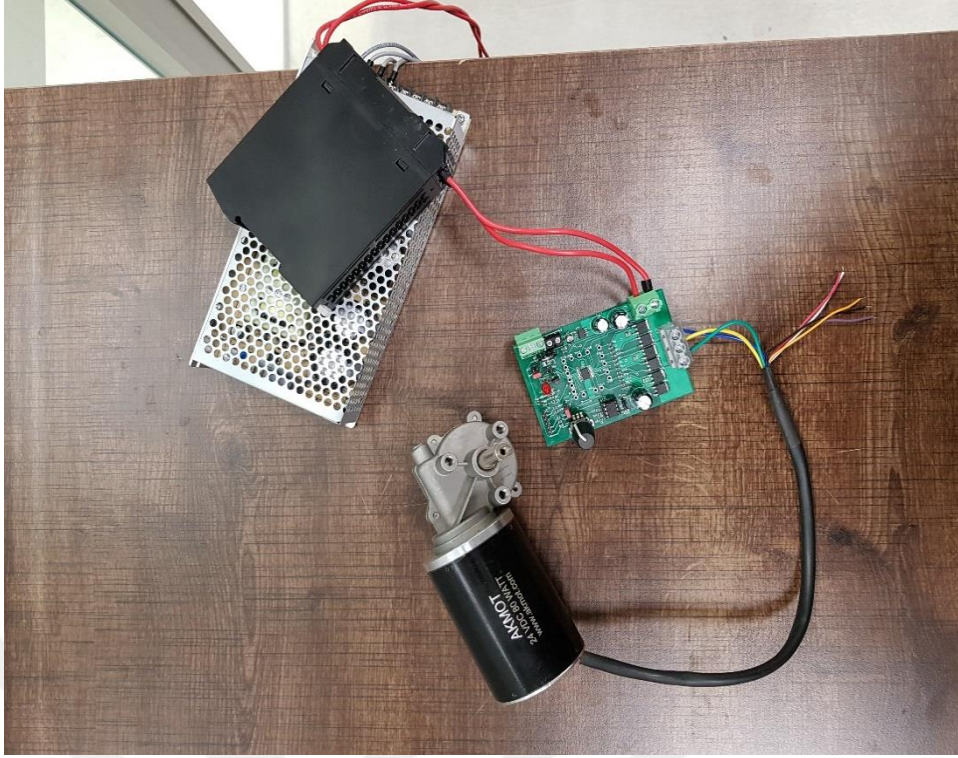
34 BLDC Sürücü PCB Dizgisi Yapılmış Halde
